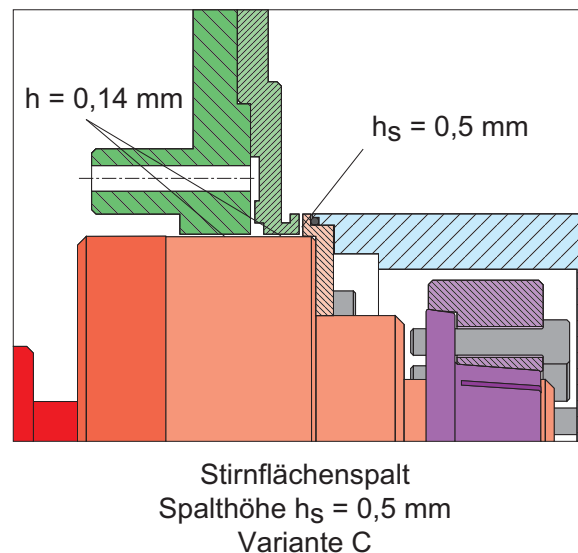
Dichtsystem mit Stirnflächenspalt (Variante C)
